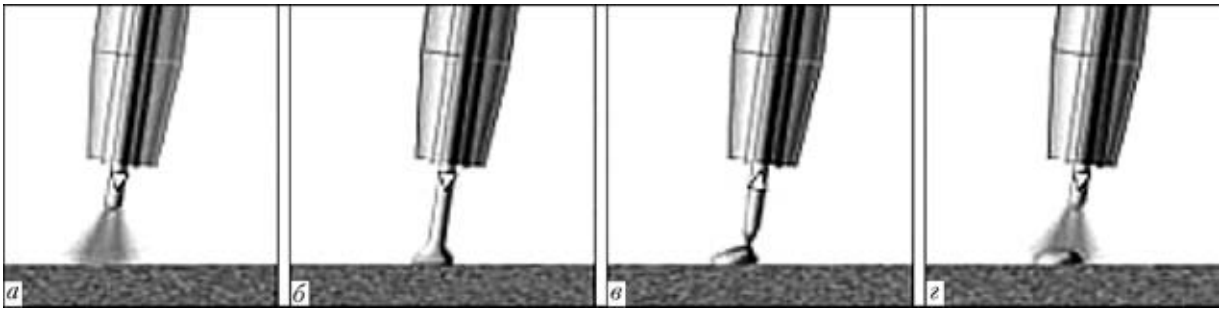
Цикл переноса электродного металла при СМТ сварке: а, б, с — движение проволоки в зону горения дуги; в — реверсивное движение
